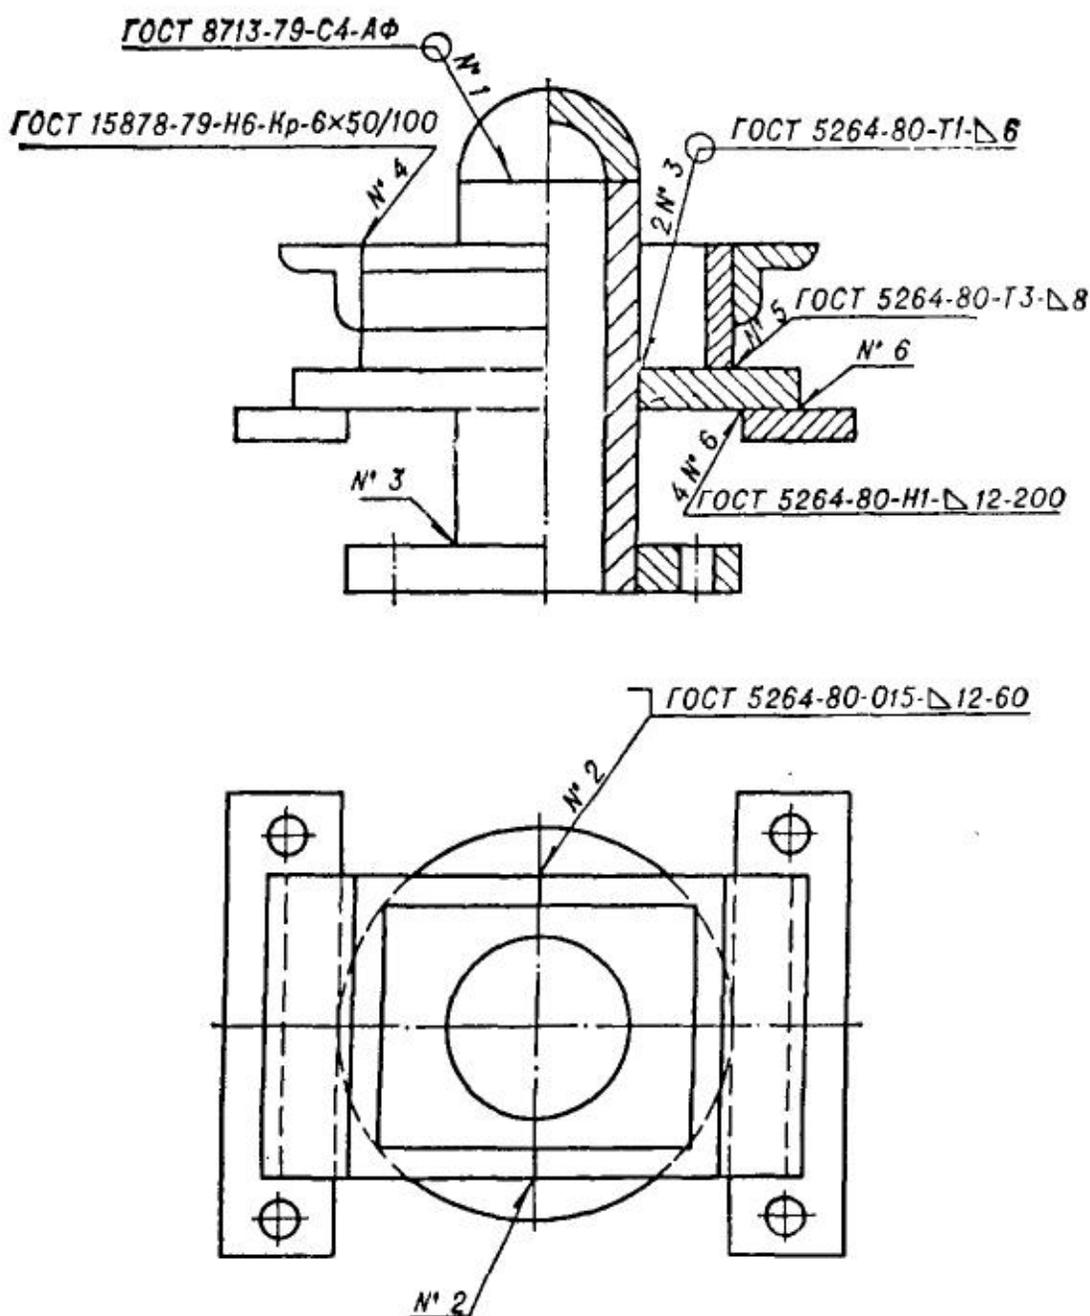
Креслення зварного з'єднання, що має однакові шви.
